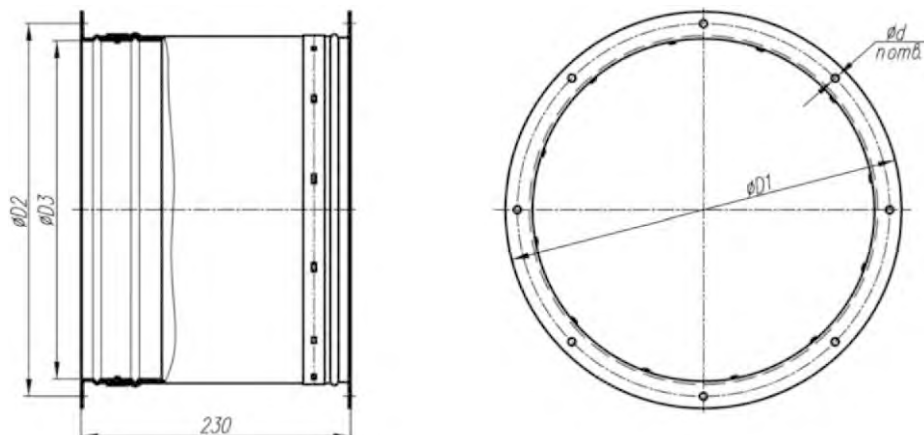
Габаритные и присоединительные размеры ГВ типа В.
